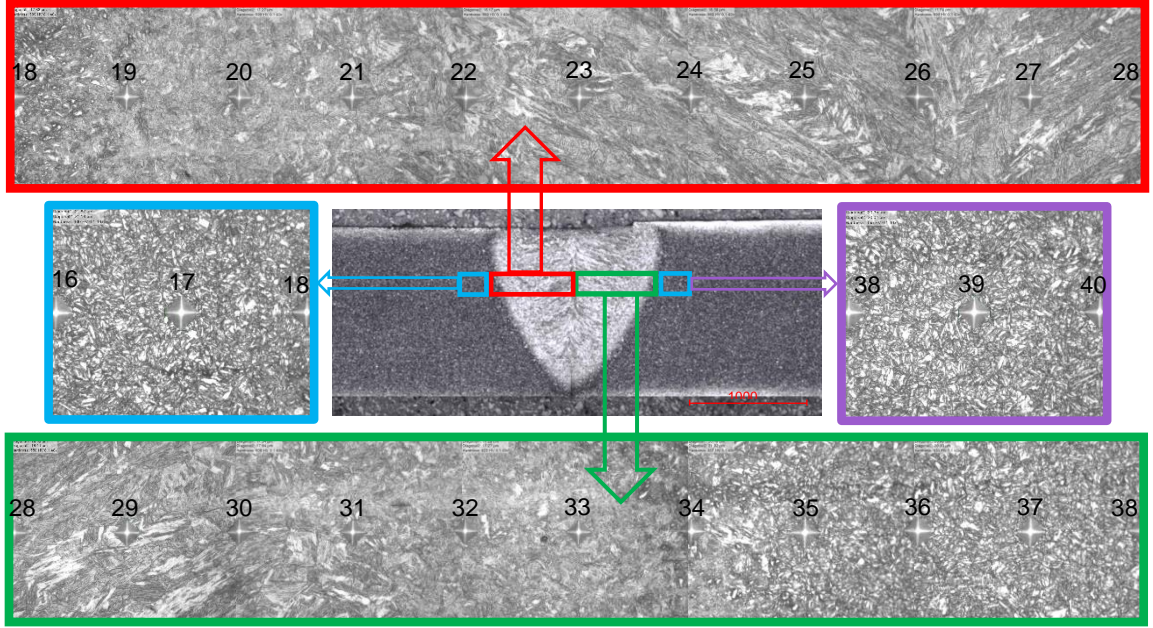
170 mm/sn hızla yapılan birleştirme (Welded sample joined with 170 mm/sec welding speed).
